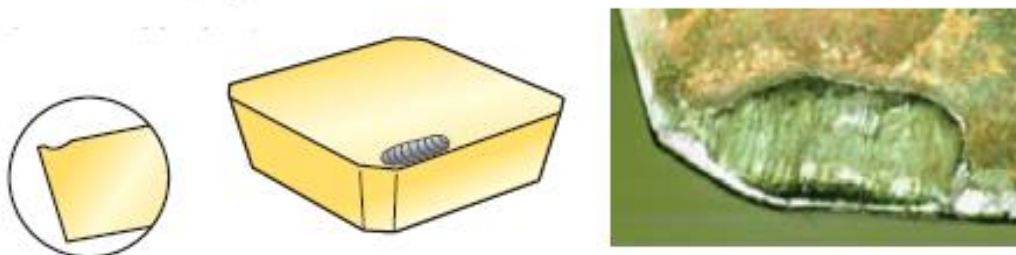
Утворення жолоба на передній поверхні ЗНБП токарного різця
